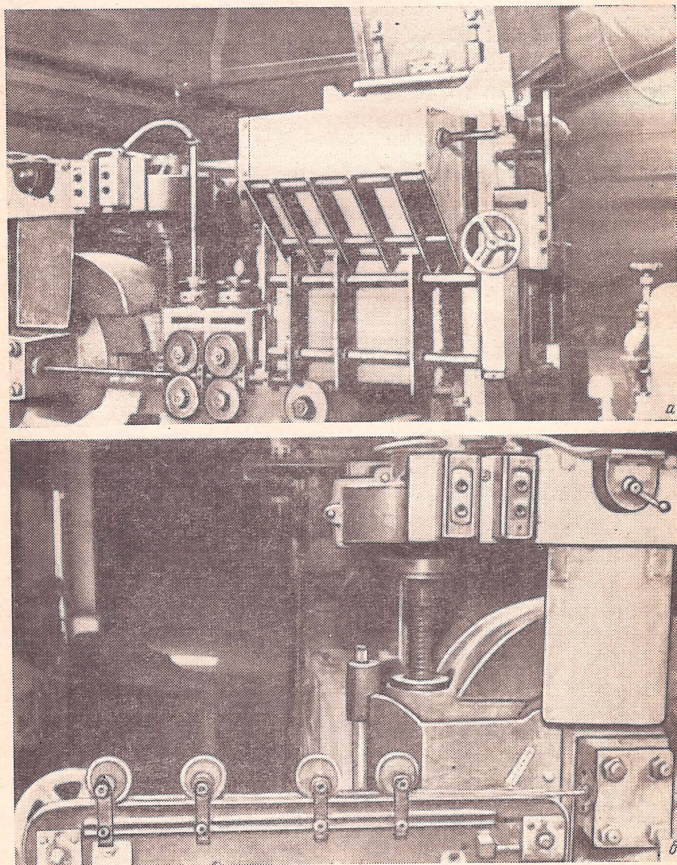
Узлы 325-т пресса для экструзии сварочных электродов
